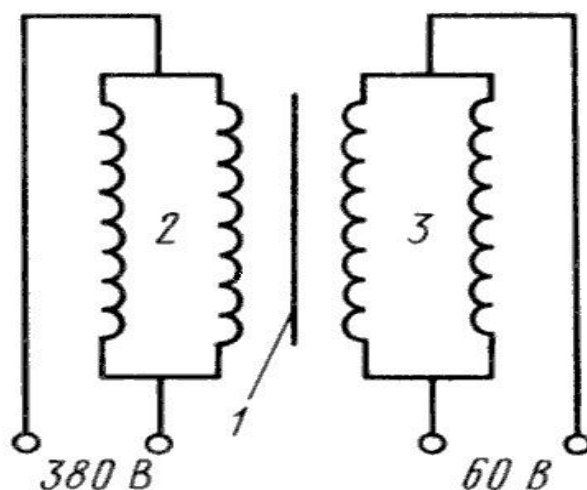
Сварочный аппарат с увеличенным магнитным рассеянием и подвижным магнитным шунтом
